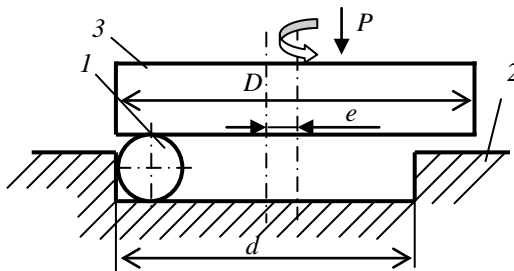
Схема накочування сферичних заготовок плоскими поверхнями
